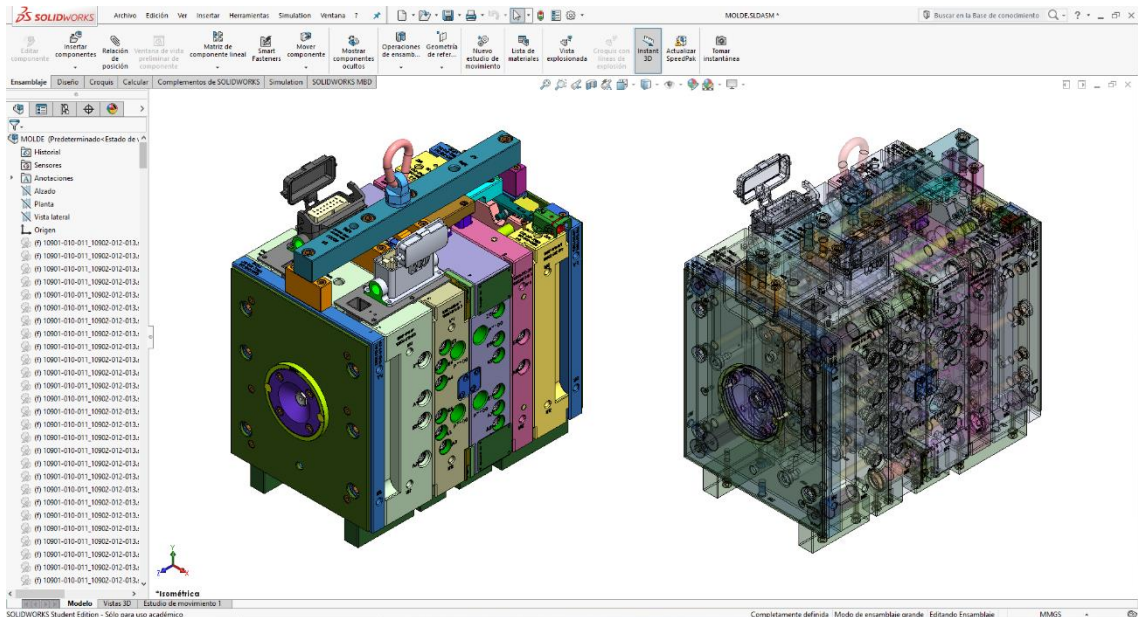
Diseño 3D - Molde 10900-023 en Solidworks
